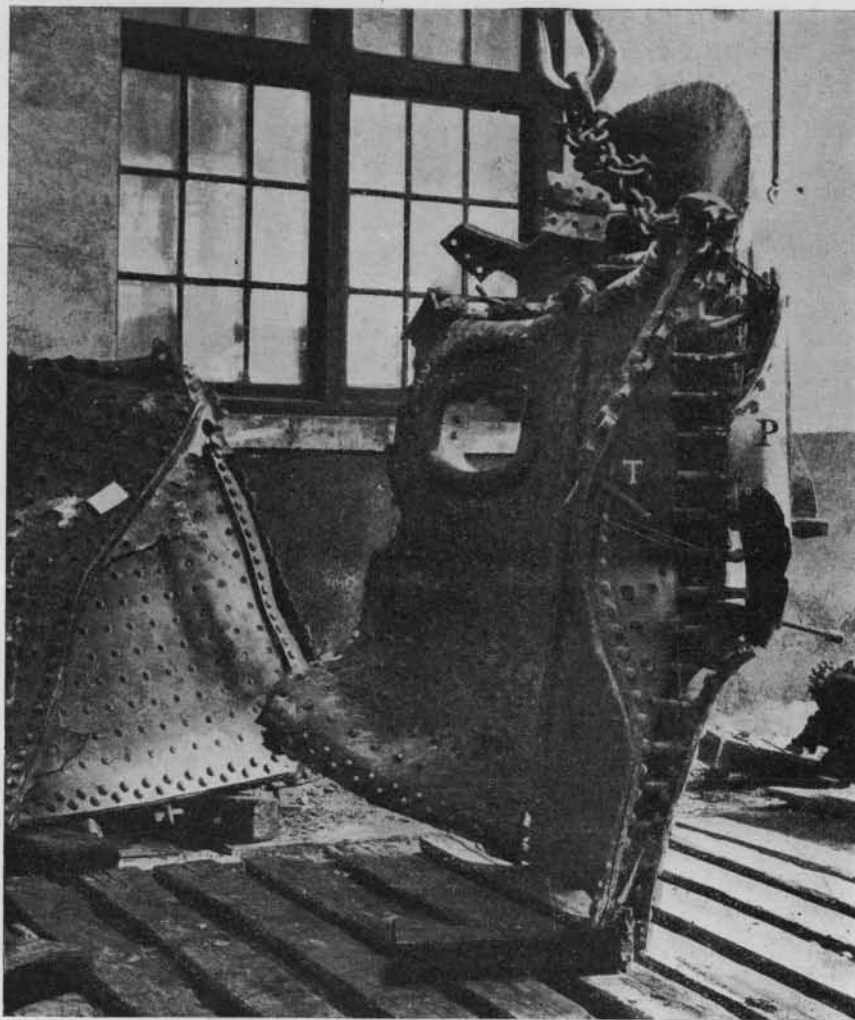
Vue latérale du flanc gauche de la boîte à feu, le panneau projeté ayant été remis à sa place.
